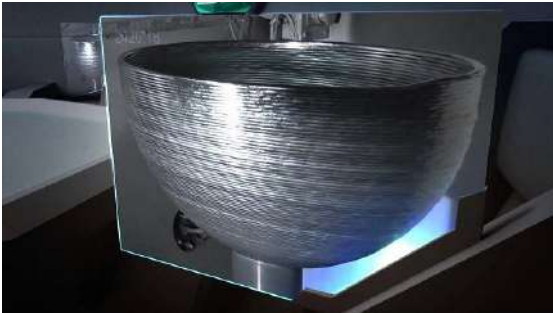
Вироби, виготовлені на 3D-принтері по металу
